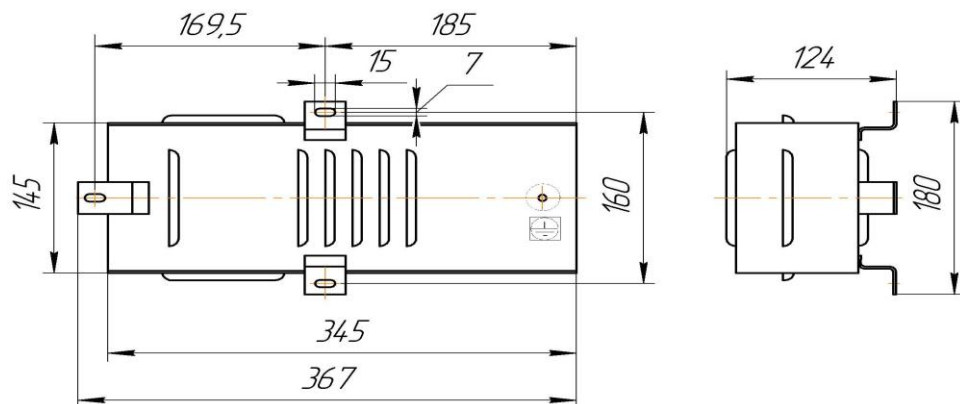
Габаритный чертеж ПЭТ-11-03
